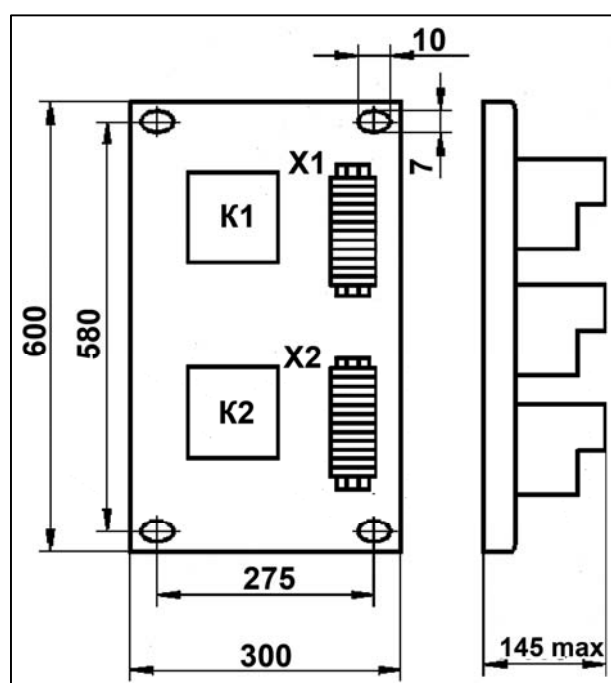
Габаритные и установочные размеры блока БРВ-2-1-У3
